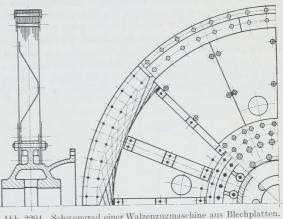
Schwungrad einer Walzenzugmaschine aus Blechplatten.
